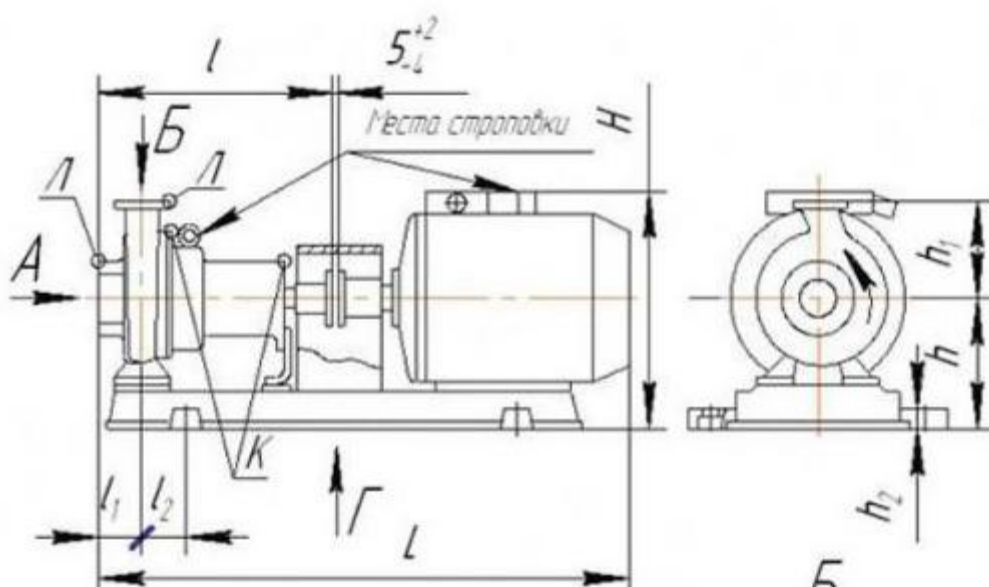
Габаритные и присоединительные размеры насоса К100-80-160
